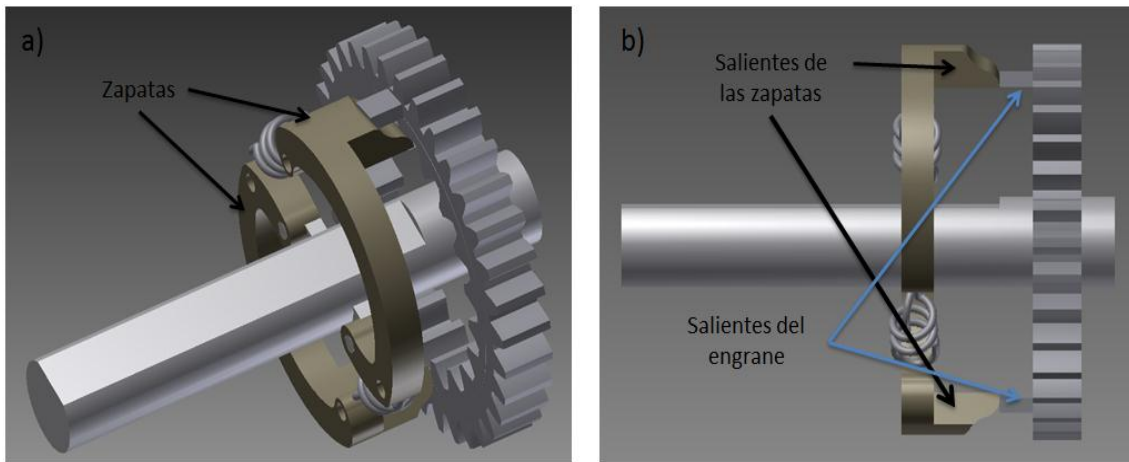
Centrífugo. a) Engrane móvil en posición inicial b) Engrane móvil desplazado
